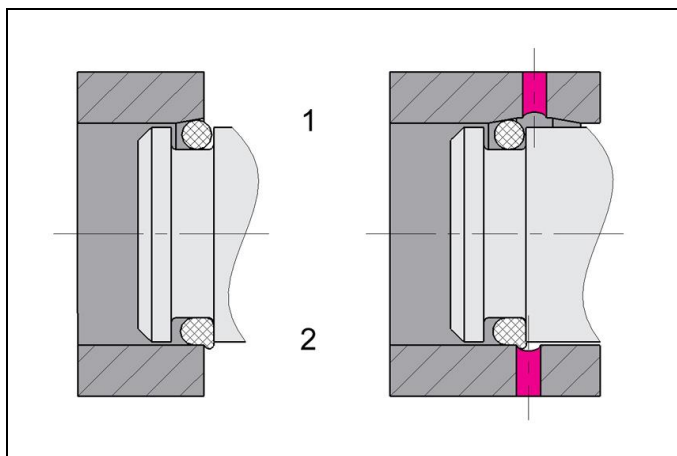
Einbau über Einführungsfasen und Querbohrung
